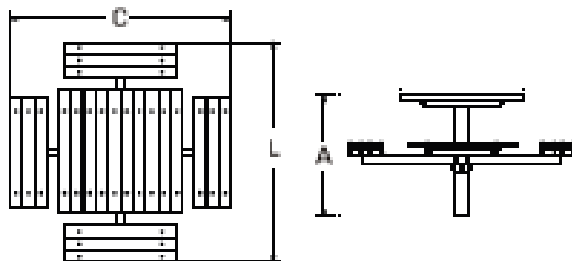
Croquis Mesa Cruz. (Fuente: <http://www.bricantel.pt/es/>)
